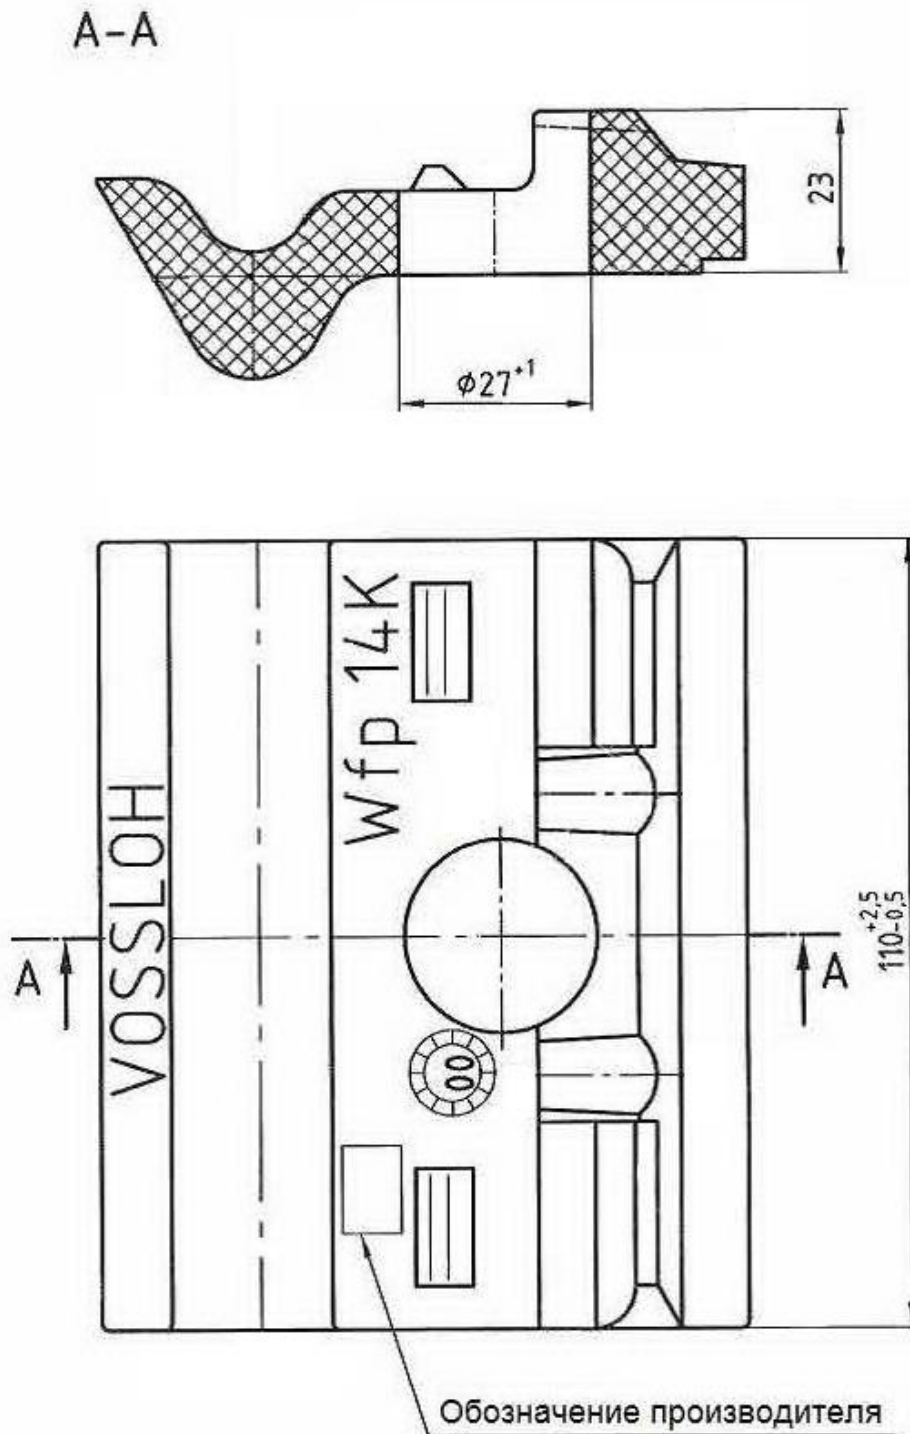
Упор боковой полимерный (все размеры для справки)
